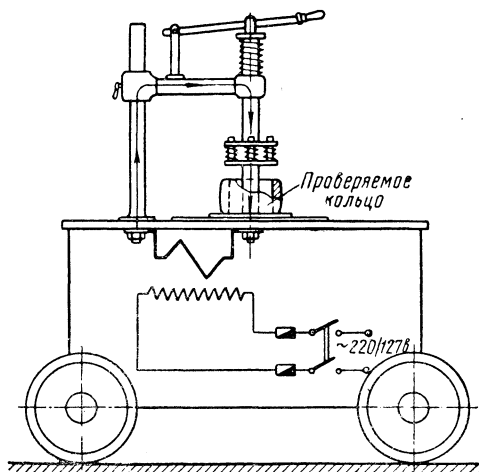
Установка для магнитного контроля колец роликовых подшипников
